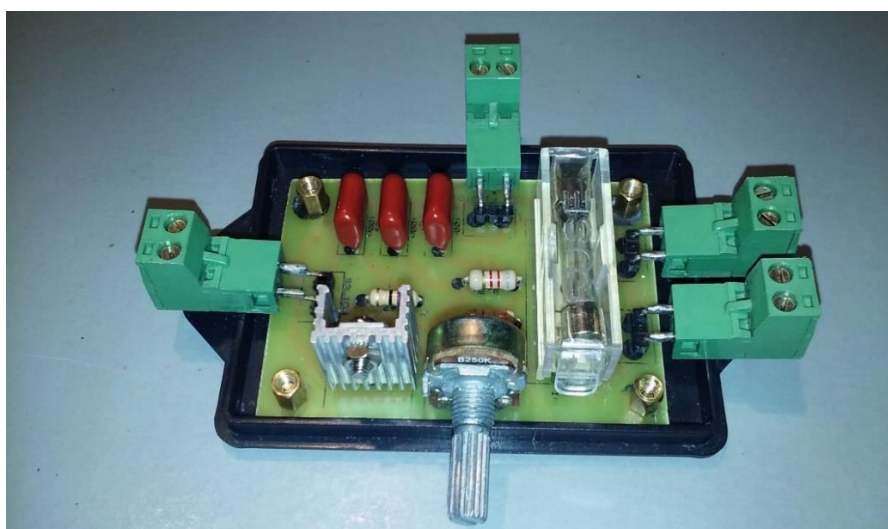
Soldadura componentes Dimmer Electrónico
